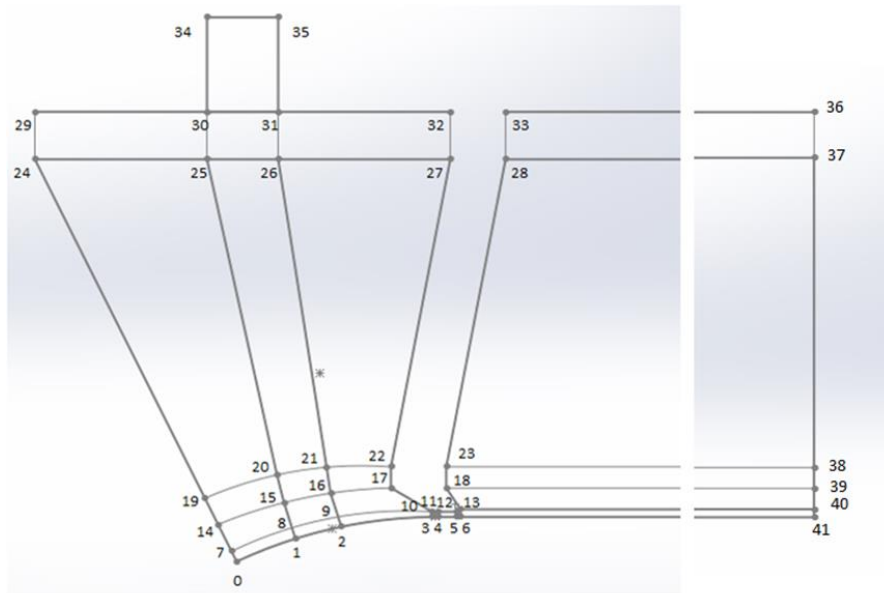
Pontos usados para criação da geometria da Faca 2, plano frontal. Existe um corte efetuado na imagem, devido ao elevado comprimento desta.
